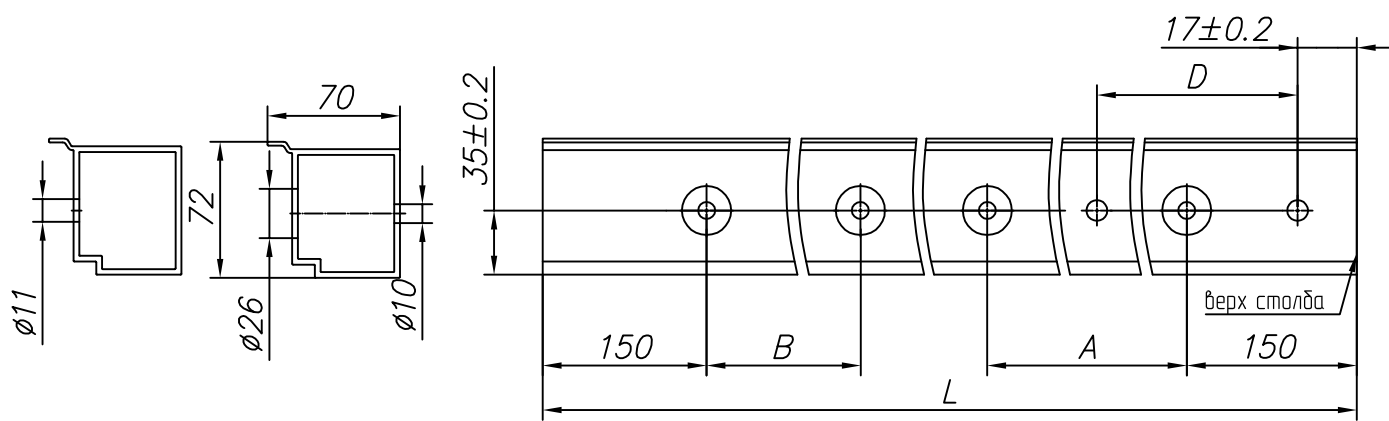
Изготовление соединителя углового FLGU.400.0914
